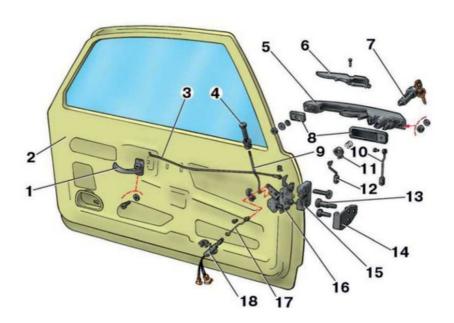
Внутреннее устройство двери автомобиля: 1 – внутренняя ручка двери; 2 – дверь; 3 – тяга внутреннего привода; 4 – кнопка; 5 – наружная ручка двери; 6 – клавиша ручки; 7 – личинка замка; 8 – уплотнитель ручки; 9 – тяга кнопки; 10 – тяга наружного привода; 11 – поводок выключателя замка; 12 – тяга поводка; 13 – «палец» фиксатора замка; 14 – корпус фиксатора замка; 15 – наружный замок; 16 – внутренний замок; 17 – тяга моторедуктора; 18 – моторедуктор блокировки замка двери
